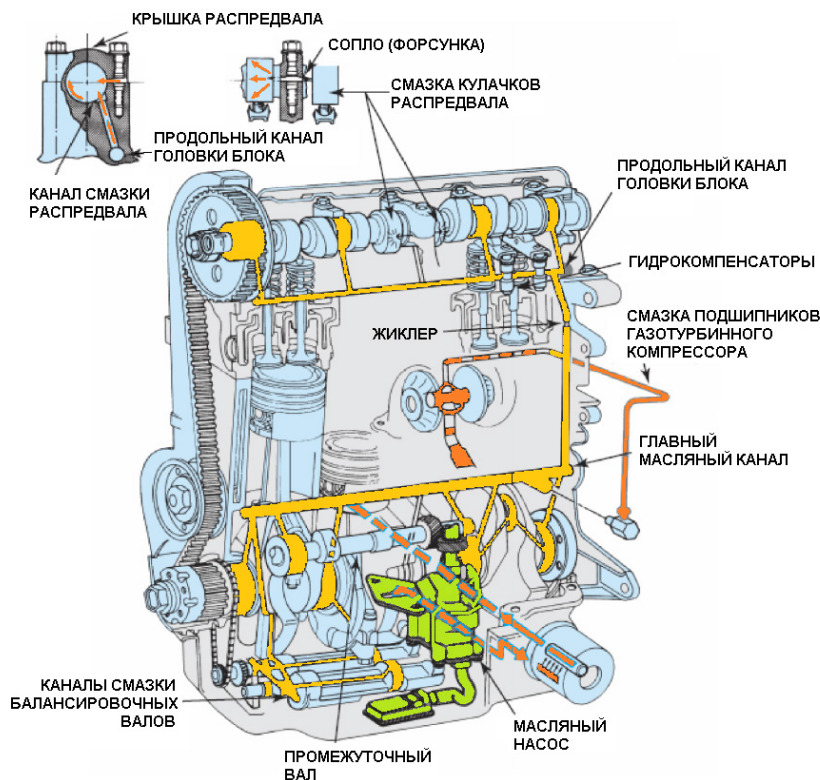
Промежуточный вал приводов масляного насоса на двигателе с верхним распределительным валом. Главный масляный канал, продольный канал головки блока и другие каналы просверлены в блоке цилиндров и головке блока цилиндров; источник: Pearson Education, Inc.
